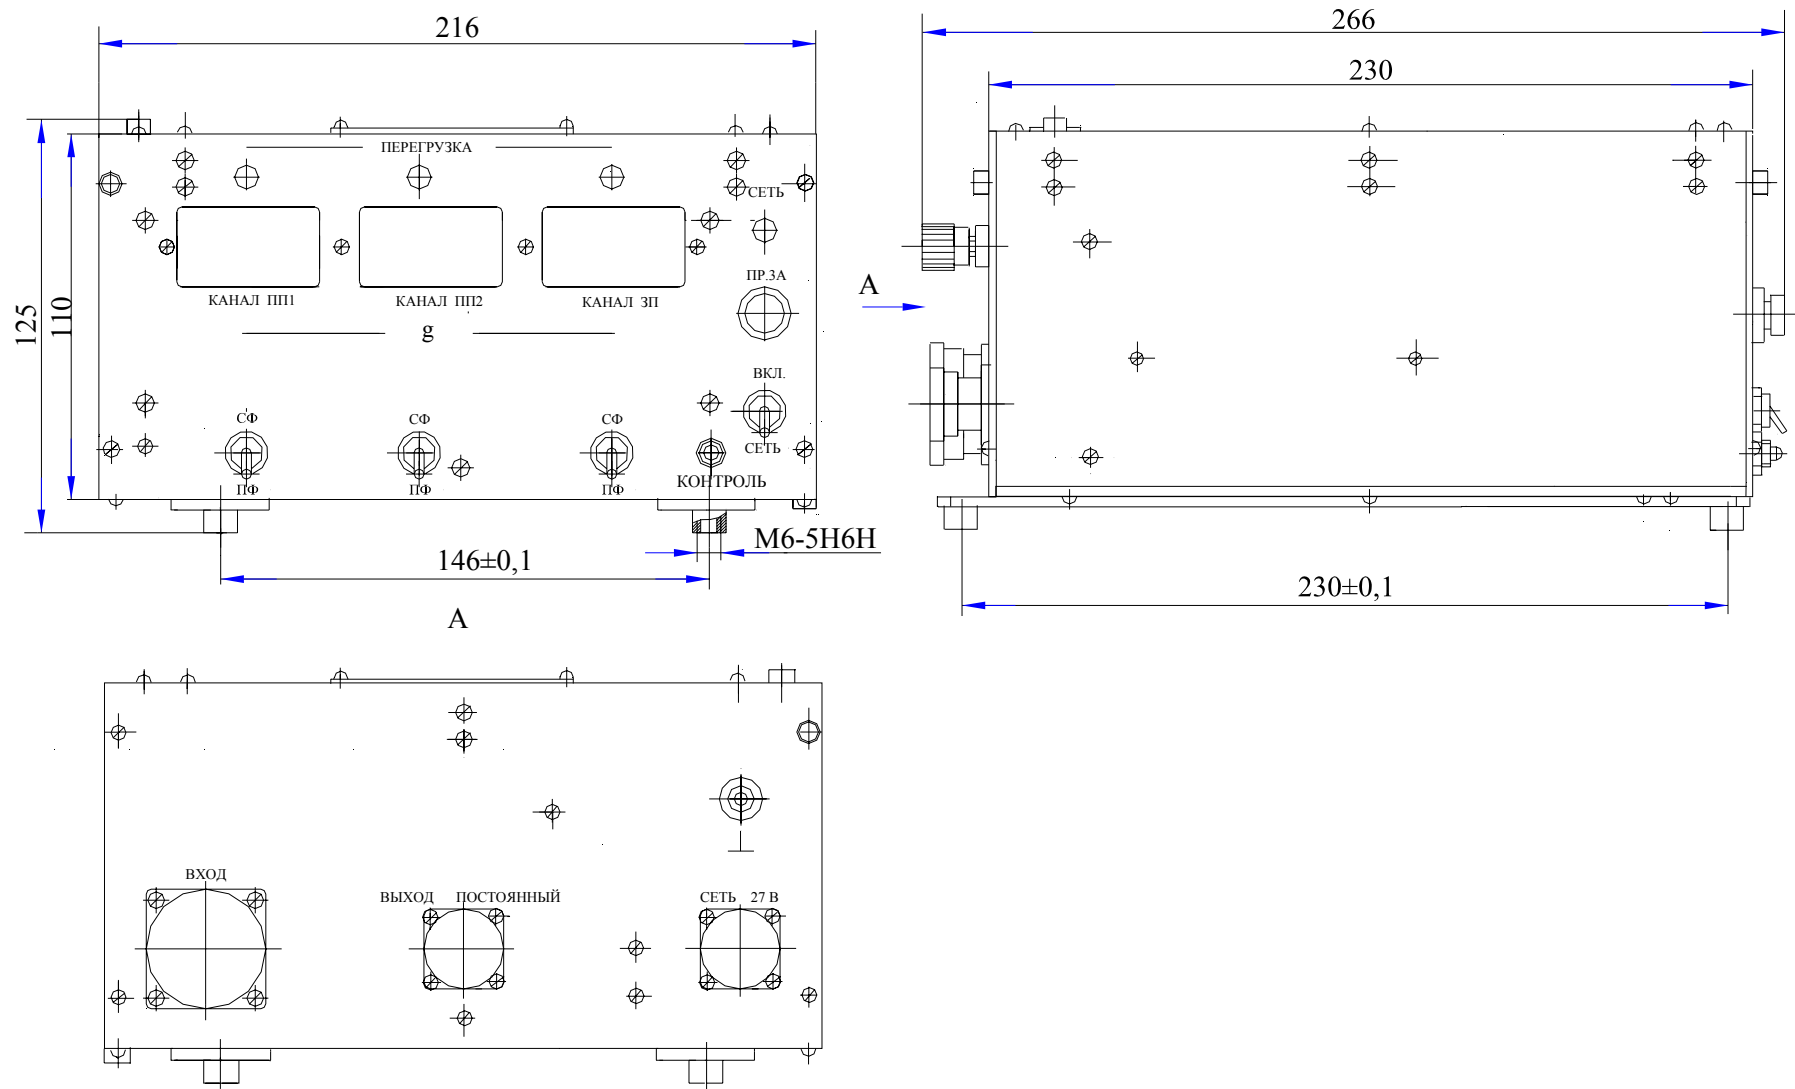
Габаритно-установочные размеры блока БЭ-39-3М.1-АИ
